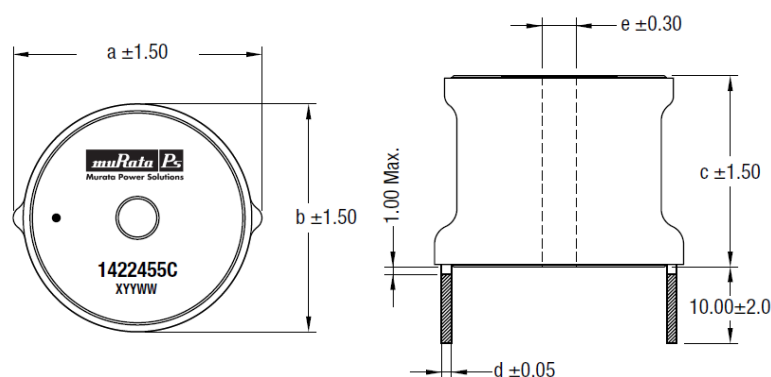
Dimensões da bobina do conversor *Boost* [34].
